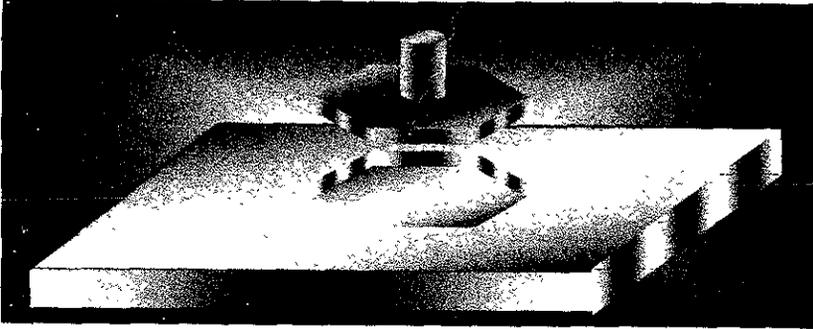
a Detalle de penetración en maquinado de metales.
